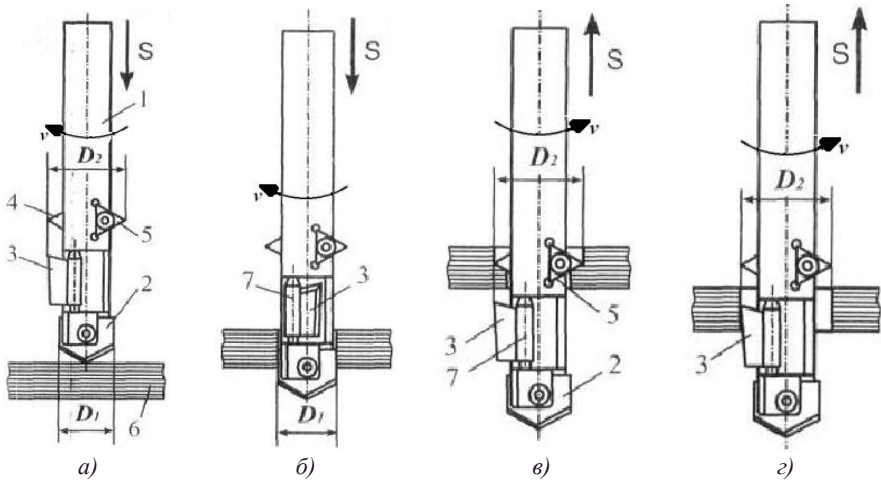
Схема обробки і схема знімання припуску комбінованим свердлом
